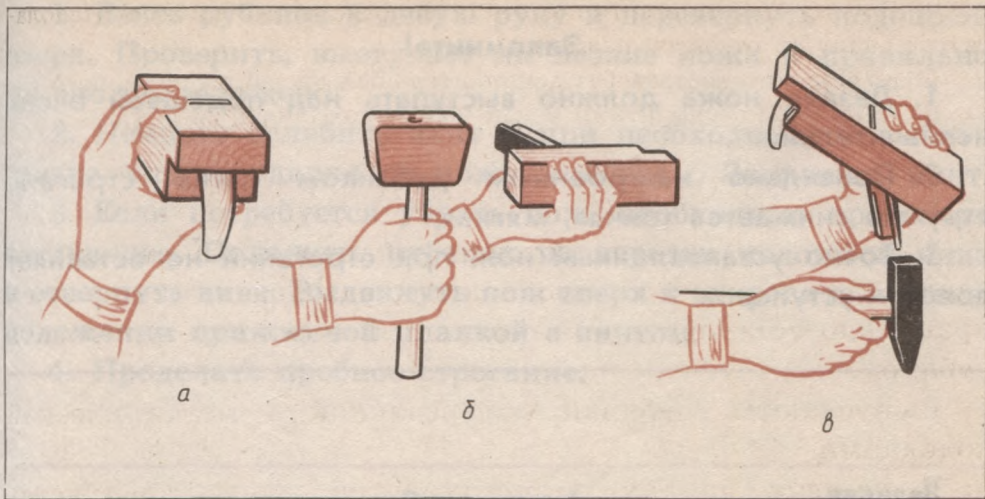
Подготовка рубанка к работе: а — проверка положения лезвия относительно подошвы; б, в — регулировка лезвия.
